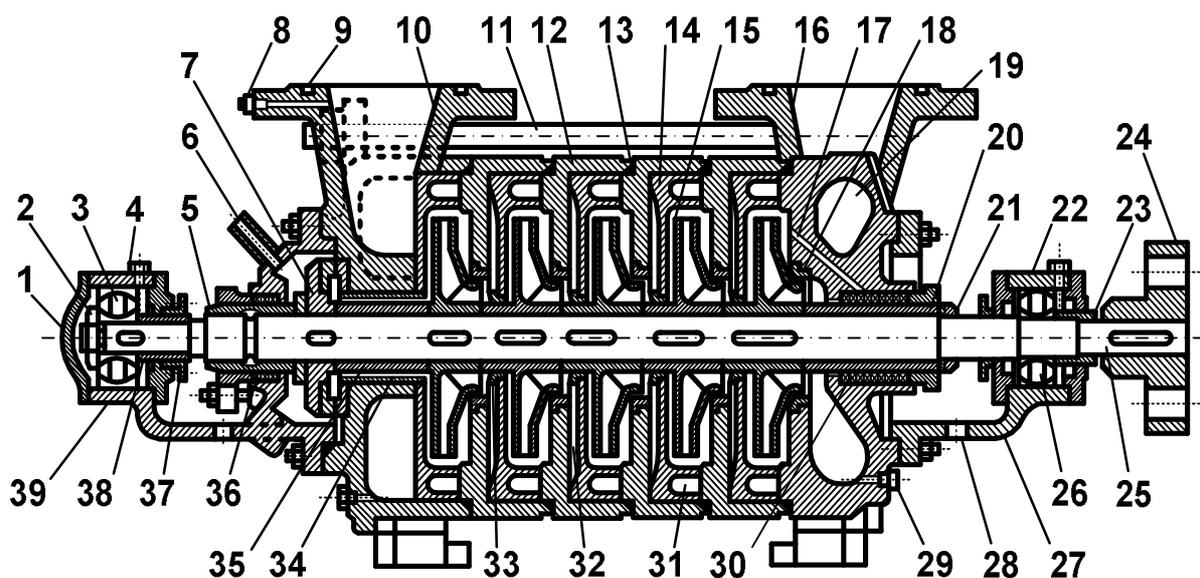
Конструкция насоса ЦНС300-300: 1 – глухая крышка; 2 и 21 – стопорная гайка; 3 и 26 – роликовые подшипники; 4 и 22 – задняя и передняя подшипниковая опоры; 5 и 20 – защитные втулки сальника; 6 – патрубок для дренажа воды из гидропята; 7 – разгрузочный диск; 8 – гнездо для установки манометра; 9 – расточка под прокладку; 10 и 16 – напорный и всасывающий патрубки; 11 – стяжная шпилька; 12 – корпус промежуточной секции; 13 – резиновое кольцевое уплотнение; 14 – спиральный направляющий аппарат; 15 – рабочее колесо 2-й ступени; 17 – канал подвода воды на гидрозатвор сальника; 18 – уплотняющее кольцо рабочего колеса; 19 – кольцевой водораспределительный канал; 23, 35 и 38 – дистанционные втулки; 24 – полумуфта; 25 – вал; 27 и 39 – передний и задний фонари; 28 – дренажное отверстие; 29 – заглушка; 30 и 36 – передний и задний сальники; 31 и 32 – спиральные каналы направляющего
